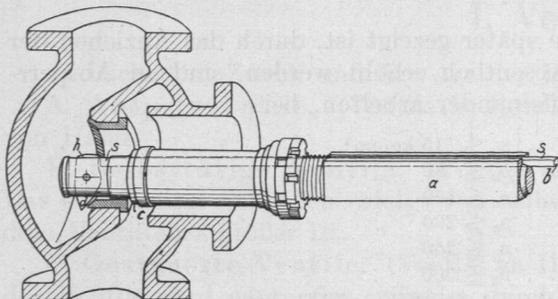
Werkzeug zum Umbördeln des Ventilsitzrandes.
